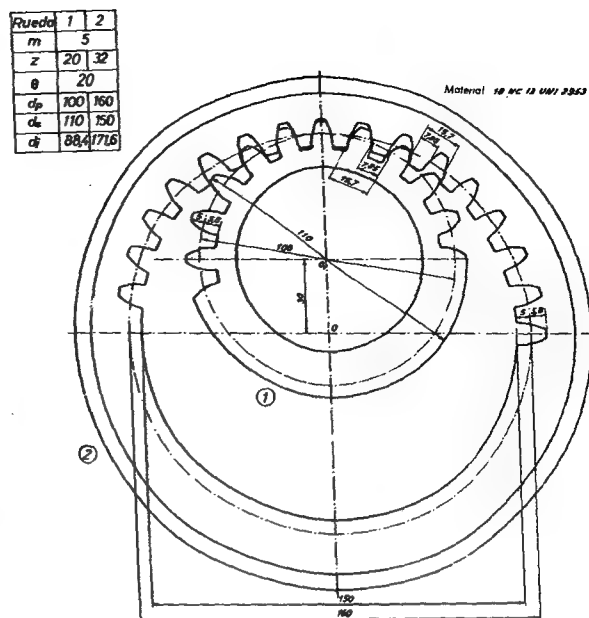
Juego de engranajes cilíndricos interiores, de dientes rectos.
